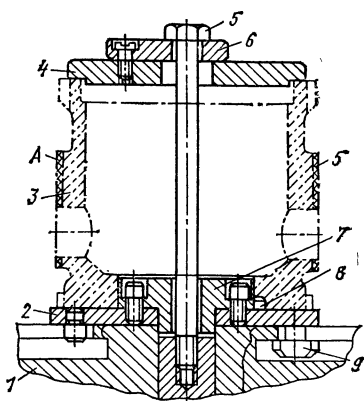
Наладка с механизированным приводом для фрезерования двух фланцев корпусной детали
